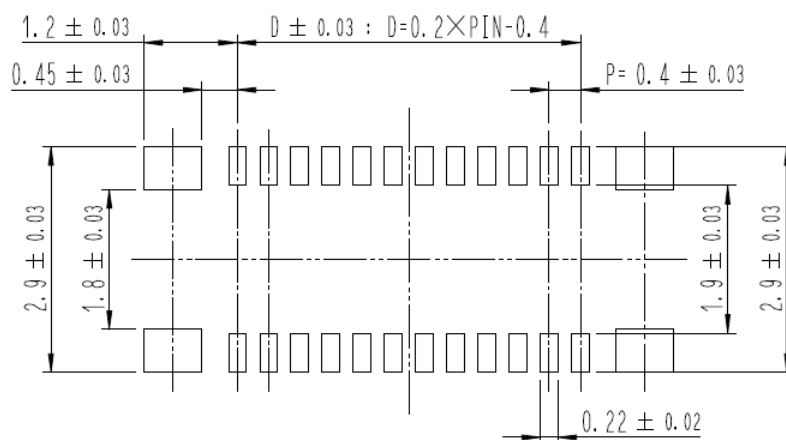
a(1) 插头连接器推荐的基板焊盘尺寸
